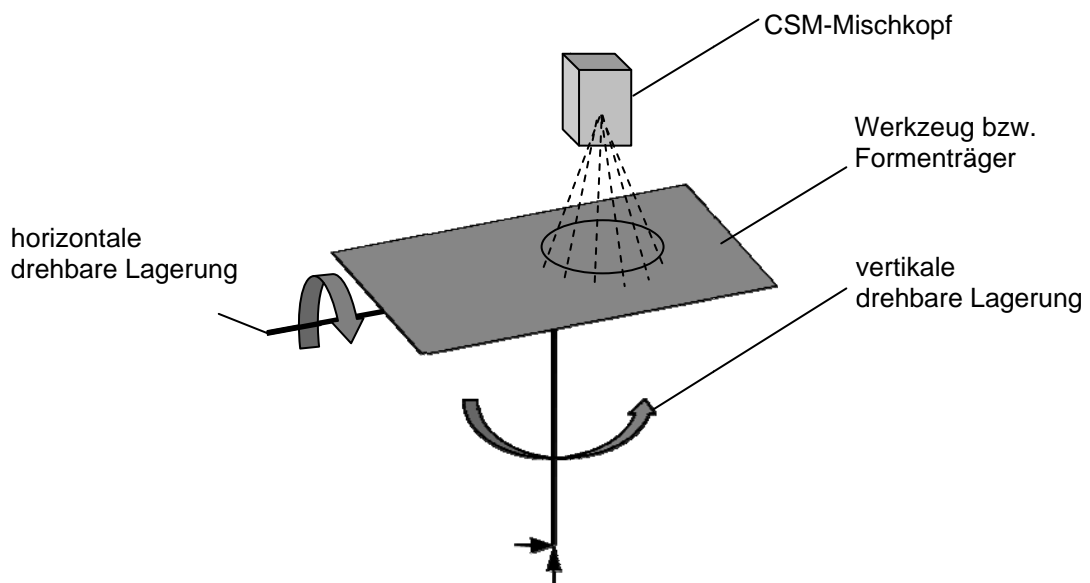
Prinzip drehbare Lagerung des Werkzeugs
